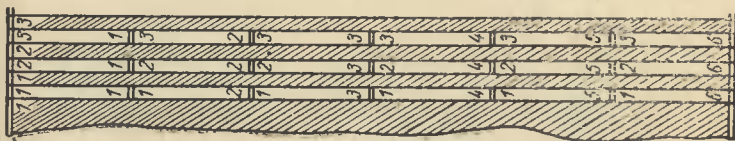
Маркировка пазовых клиньев и зубцов ротора.
